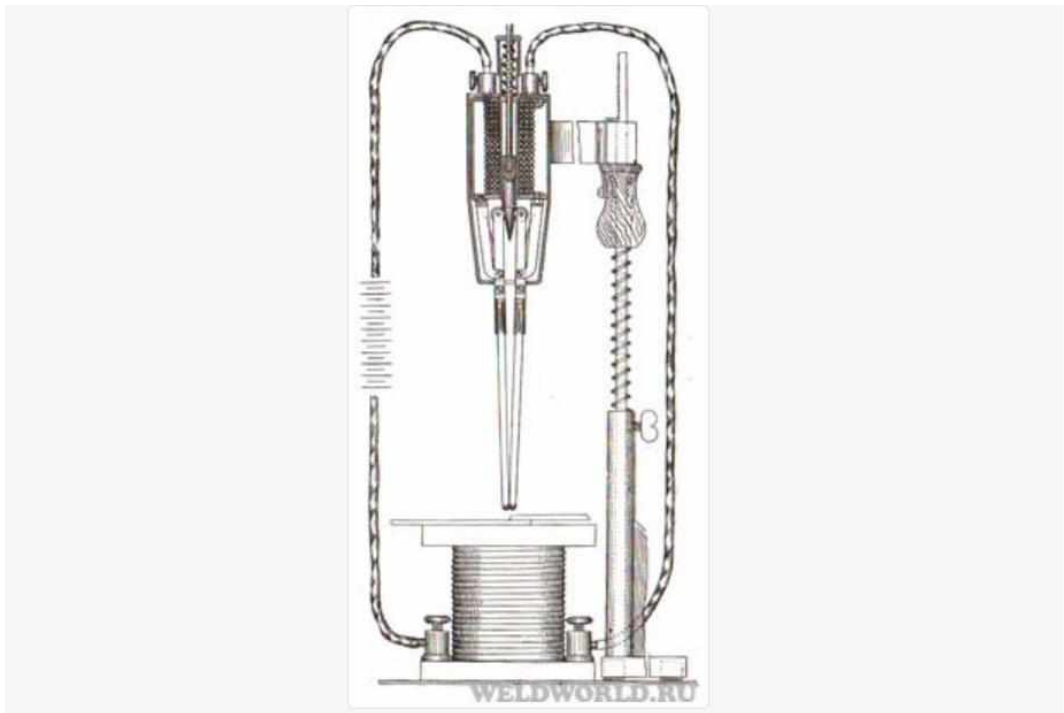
Dispositivo de soldagem a arco indireto com regulador automático de comprimento de arco – Weldworld.ru
